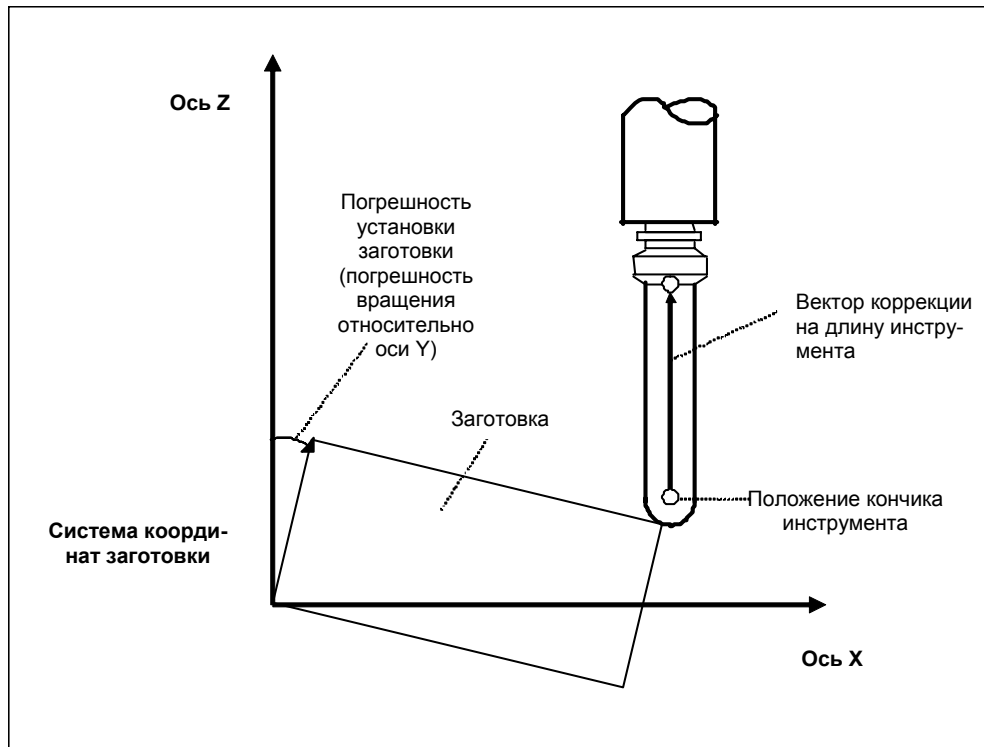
(g) Резка вершиной инструмента, когда имеется погрешность установки заготовки (если RCM=0)
